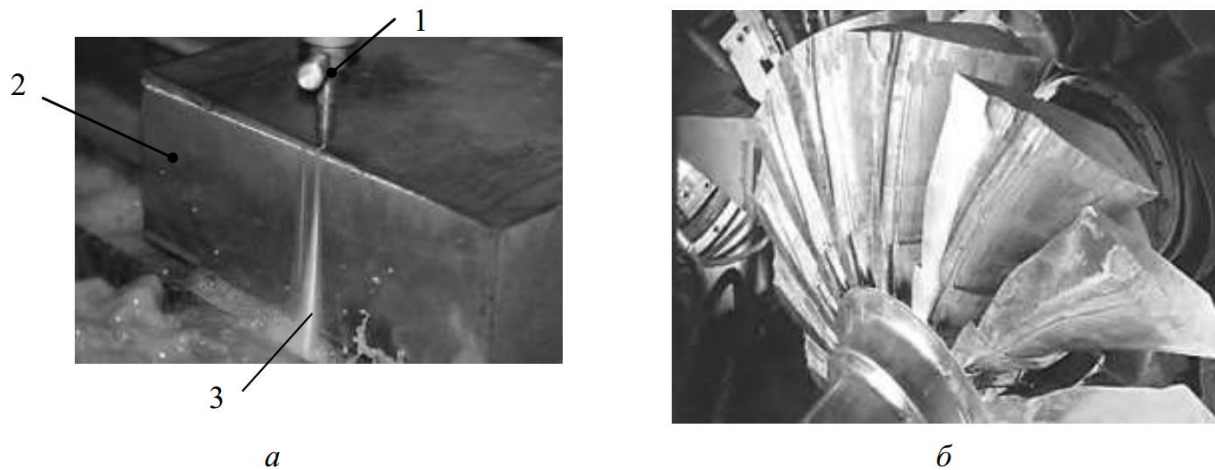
Гідроабразивна обробка міжлопаткових каналів робочих коліс турбін [100]: а – приклад обробки; б – робоче колесо після обробки;
